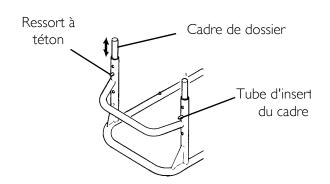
Régler la hauteur du dossier - Dossier large uniquement
